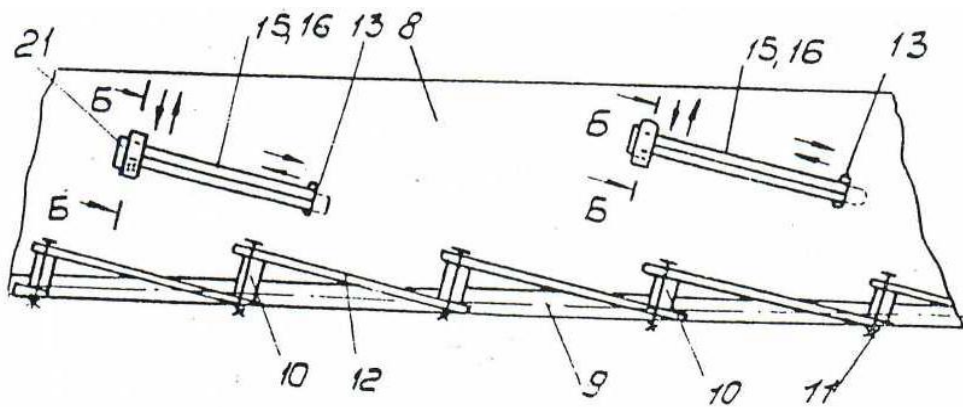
Розгорнута бокова стінка барабана, вид збоку
